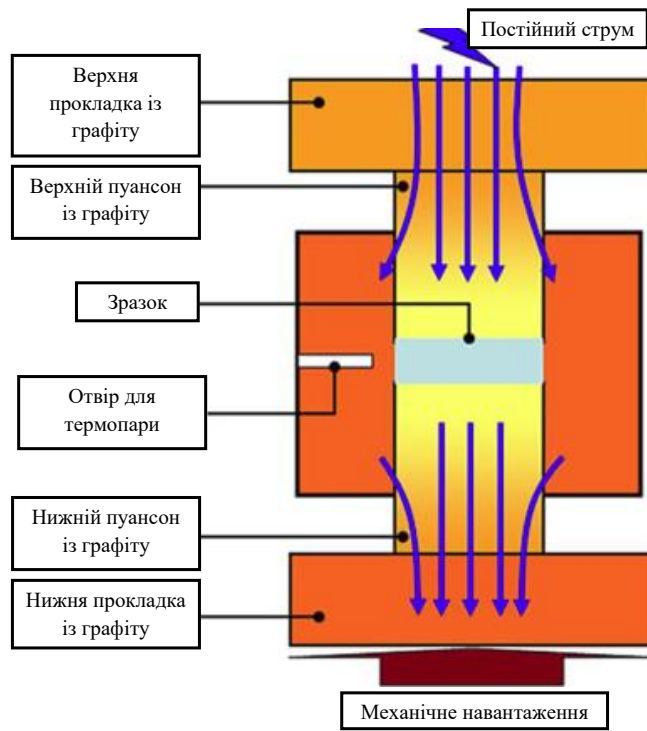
Схематичний розріз прес-інструмента [9]
